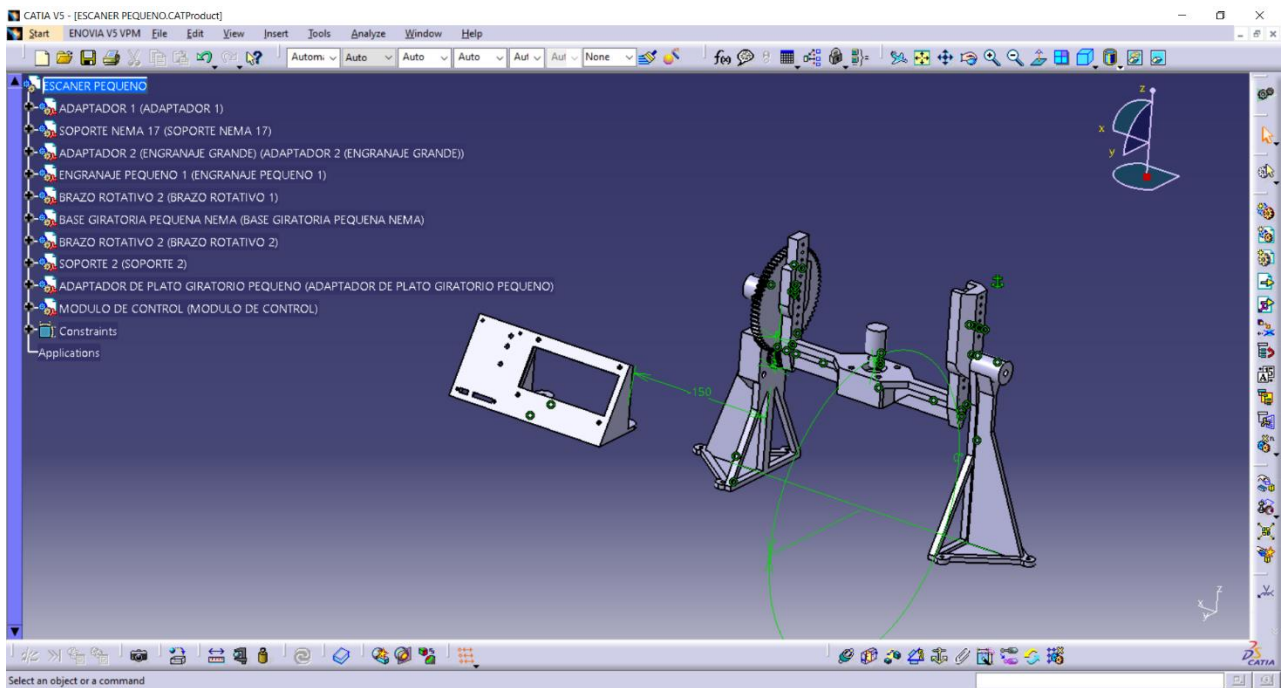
Escáner 3D montado en Módulo Assembly Desing con restricciones visibles
